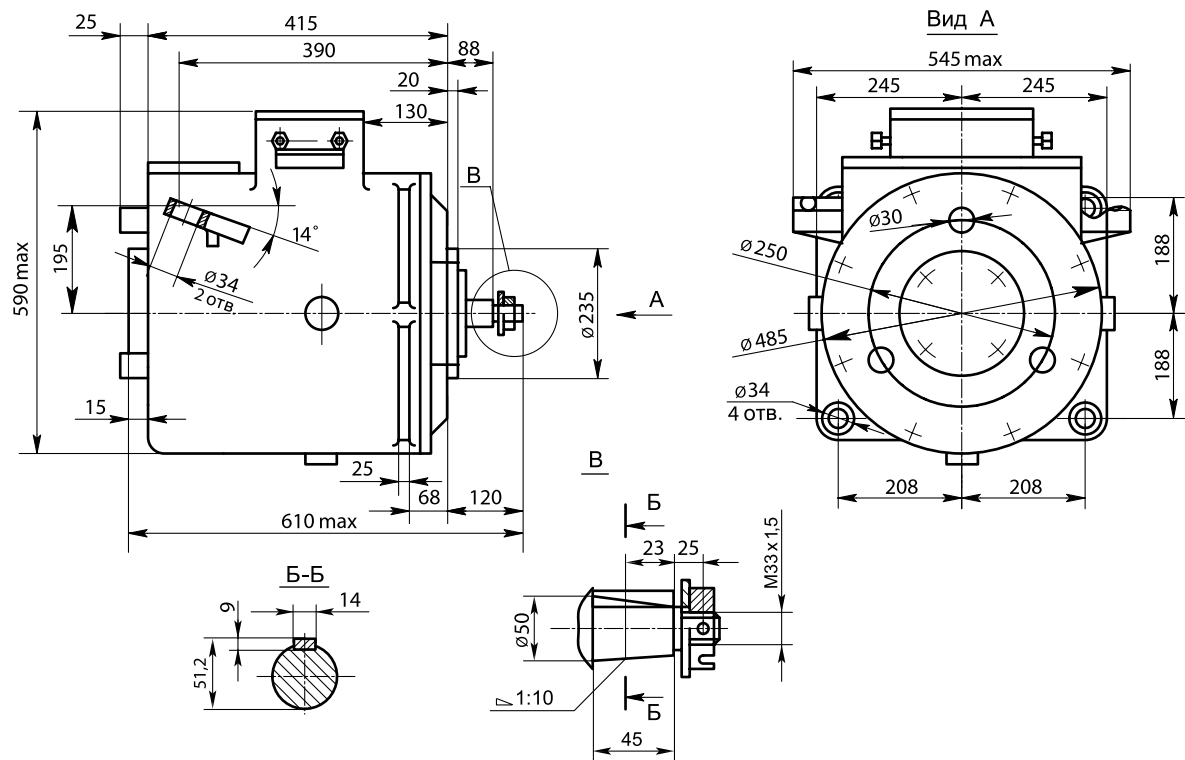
Габаритные и установочные размеры электродвигателя ДРТ-14
